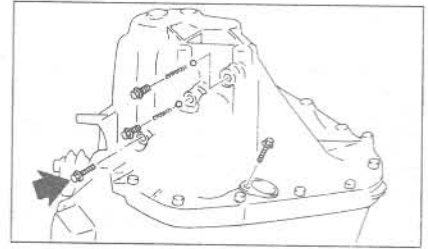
Откручивание болта промежуточного вала заднего хода (отмечен стрелкой), пробки фиксаторов и болта выключателя положения (Глава 12)
